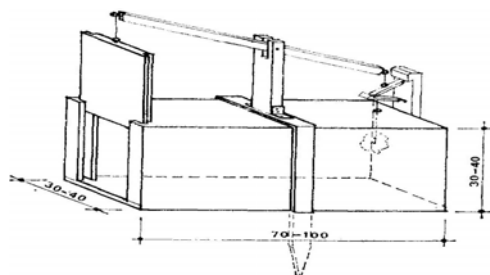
Truhlík a detail spouštěcího zařízení
